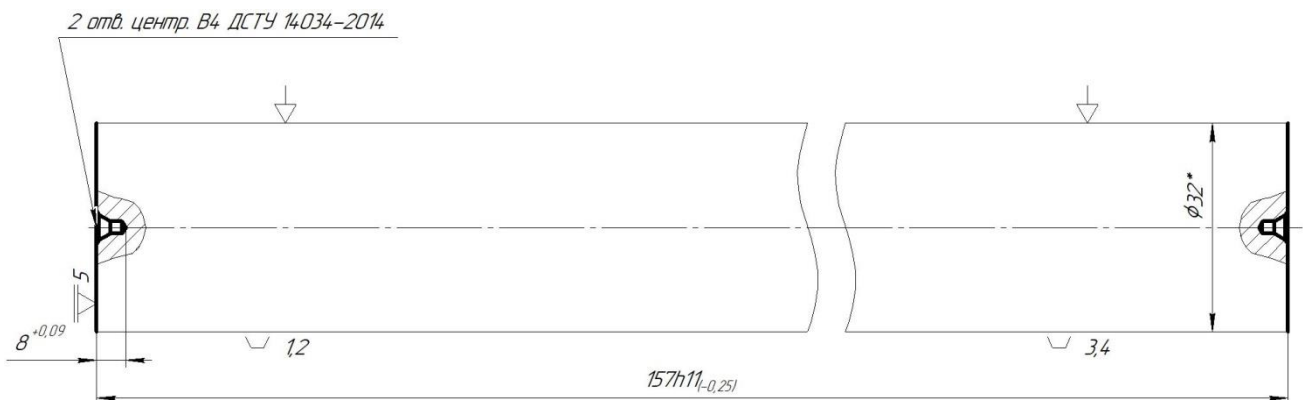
Схема установки заготовки на призми з притиском прихватами
